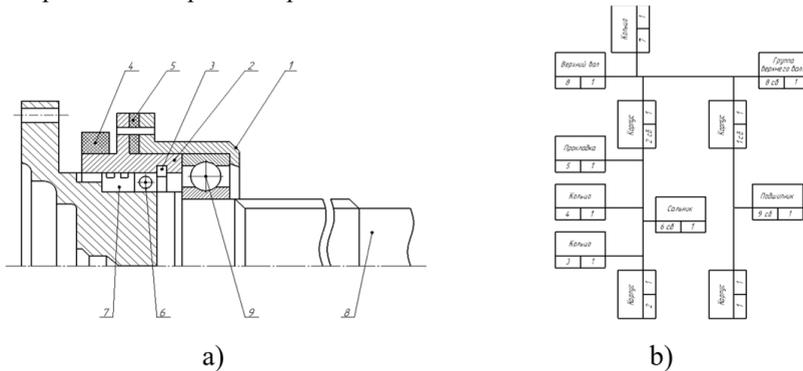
Фрагмент чертежа (а) и схема сборки (б) узла «верхний вал коробки передач»
